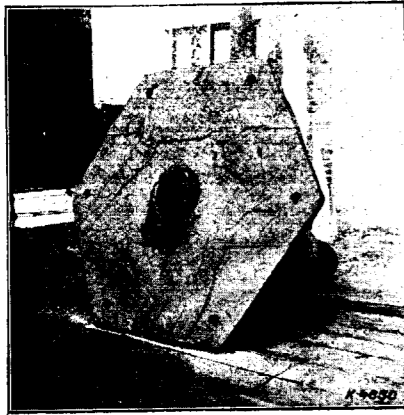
Silla de la fig. 20 reparada con soldadura por arco.
